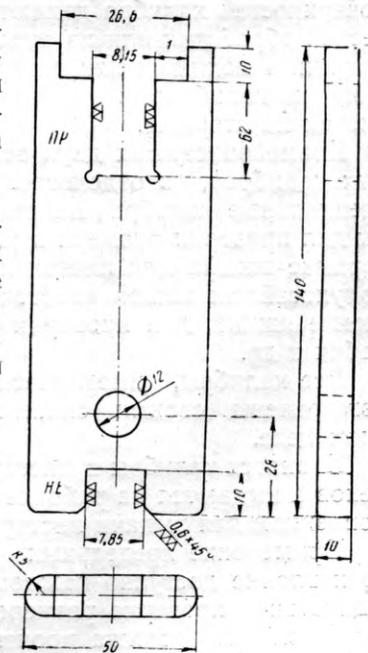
Предельный калибр для контроля размеров шипов и заплечиков деталей шкафа КЛ-4001
